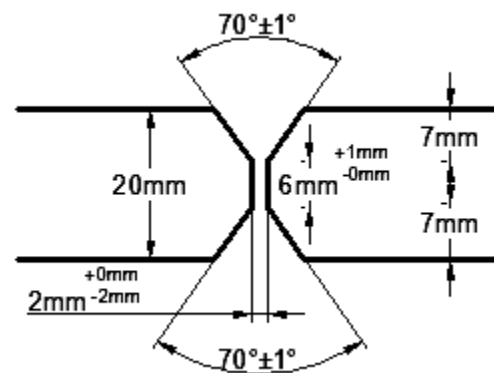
DIMENSIONES Y TOLERANCIA DE LA JUNTA
